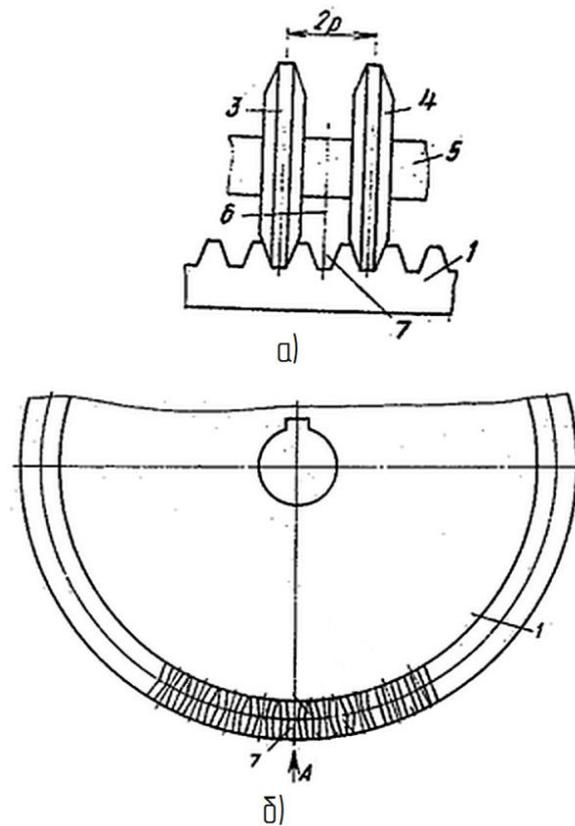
Способ нарезания плоского колеса: 1 – плоское колесо; 3 и 4 – дисковые модульные фрезы; 5 – оправка; 6 – середина инструмента; 7 – впадина между зубьями
